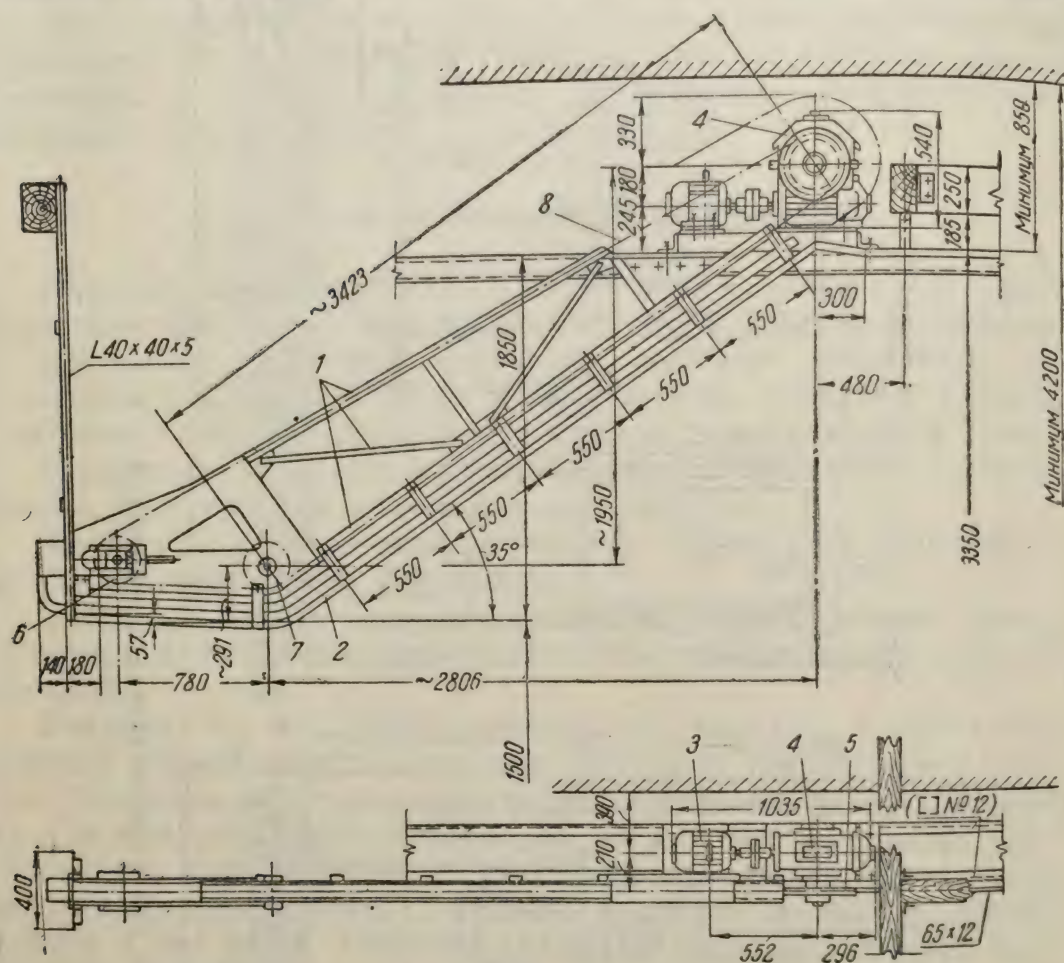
Цепной элеватор для подъема свиных туш на полосовой путь:
